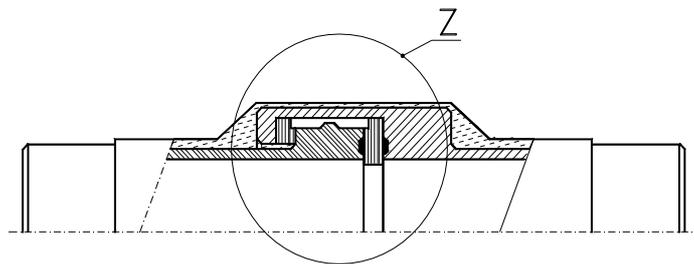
Montage einer Funkenstrecke über einer isolierenden Flanschverbindung
